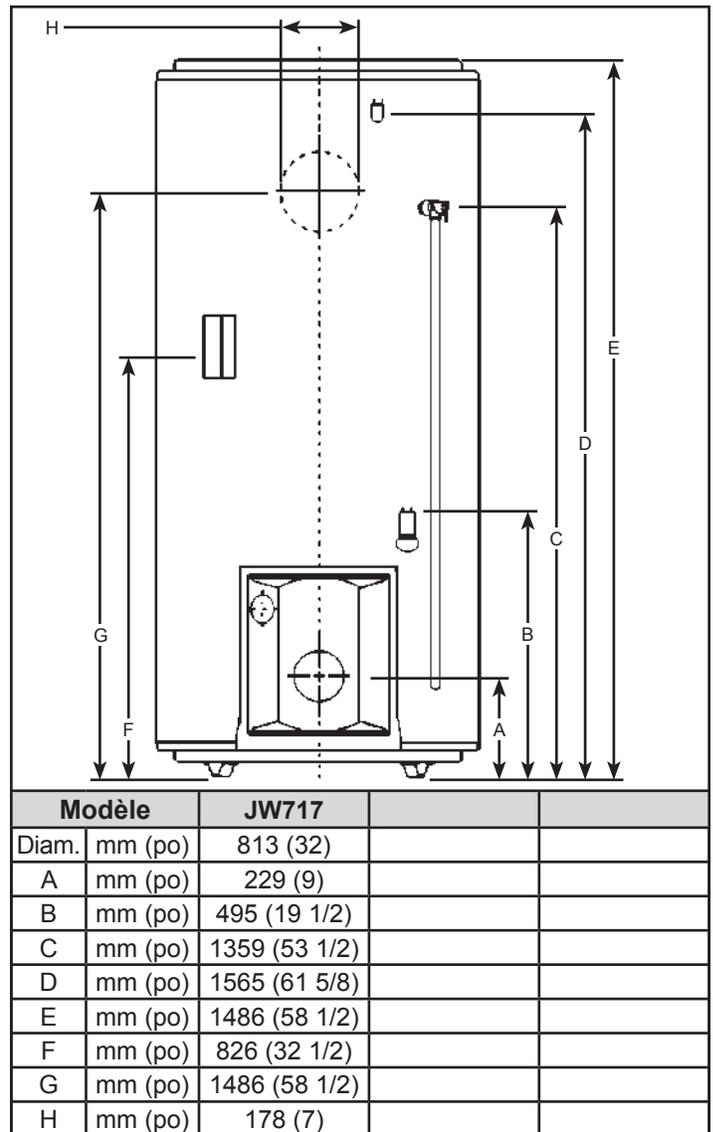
Dimensions d'installation (modèles à cheminée de fumée arrière)
